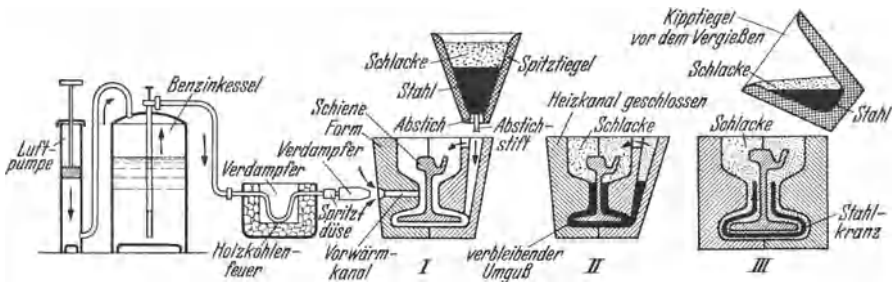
Einrichtungen für die Thermitschweißung.
